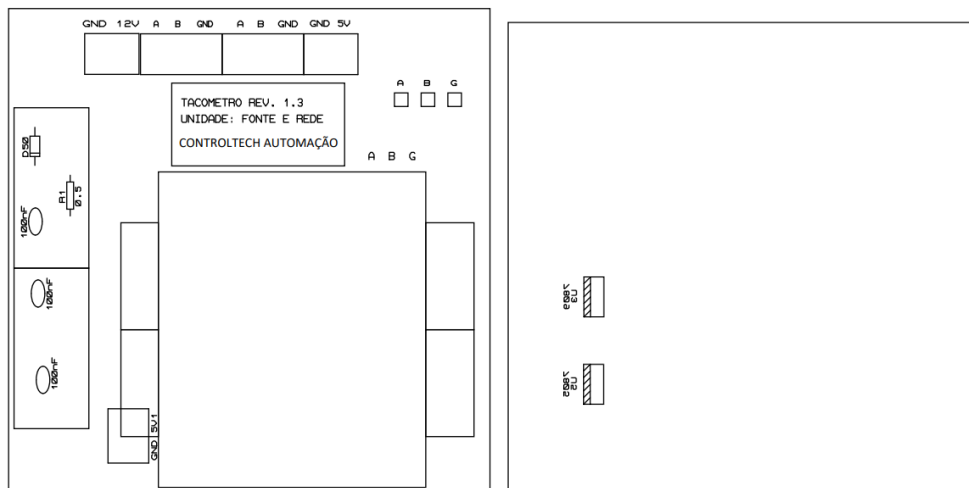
Vista superior e inferior PCB REDE Ver. 1.3
